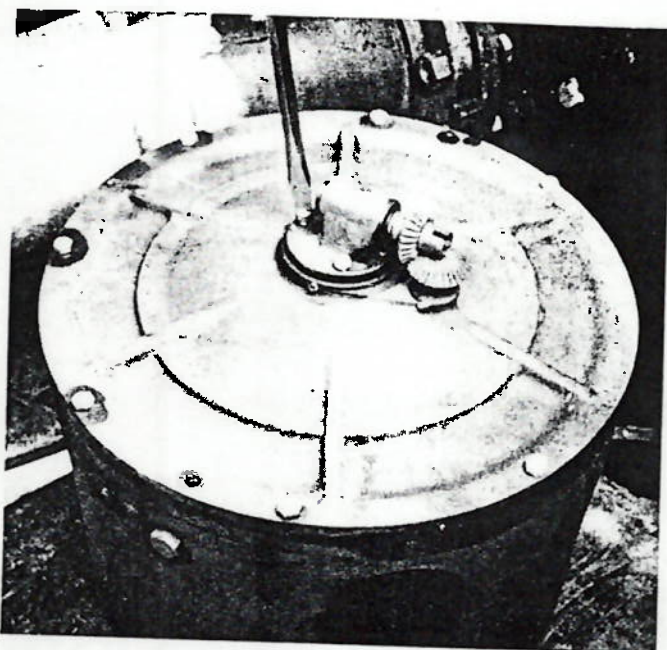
REMOCIÓN DEL ENGRANAJE Y DEL BLOQUE DEL COJINETE.
